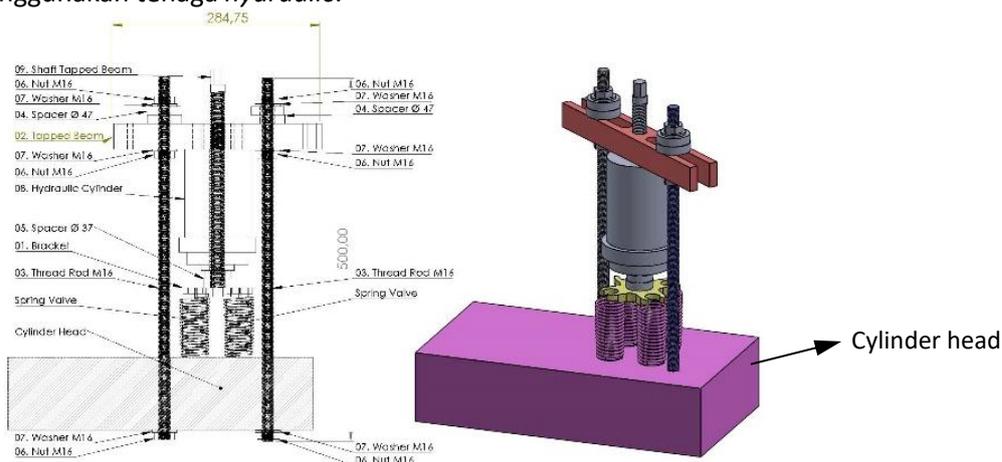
Special tool remove dan install valve spring dengan 2 valve spring sekaligus
